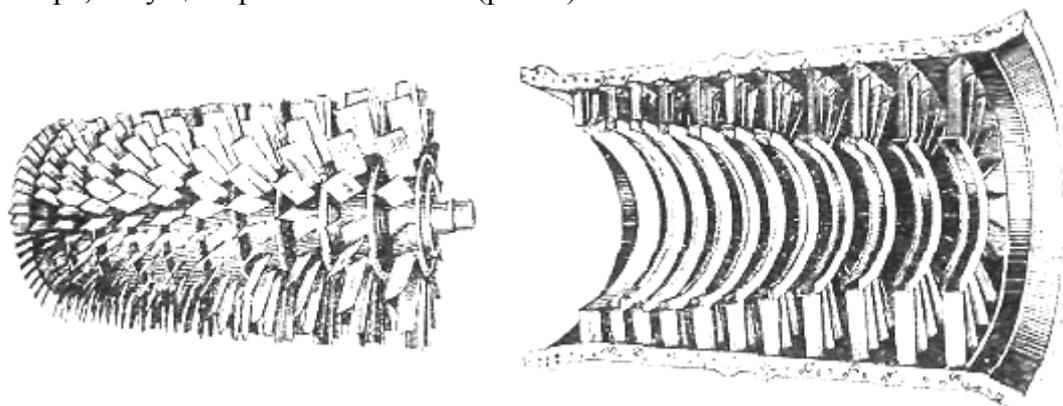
Ротор и корпус 11-ти ступенчатого осевого компрессора
